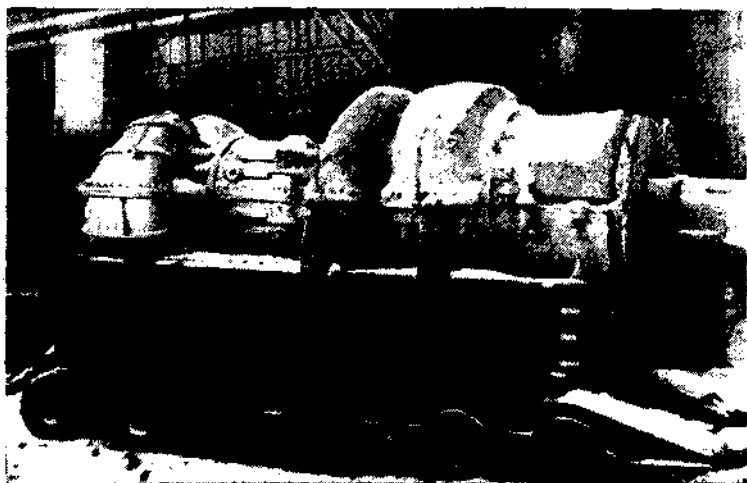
Турбоагрегат газотурбинной компрессорной установки
